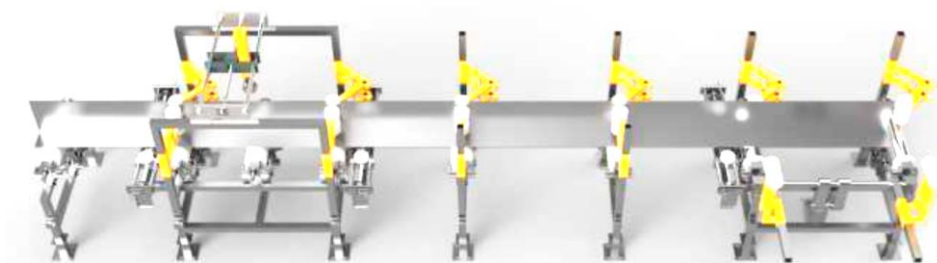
Equipamento para produzir perfis em "T" por soldadura a laser [1].
